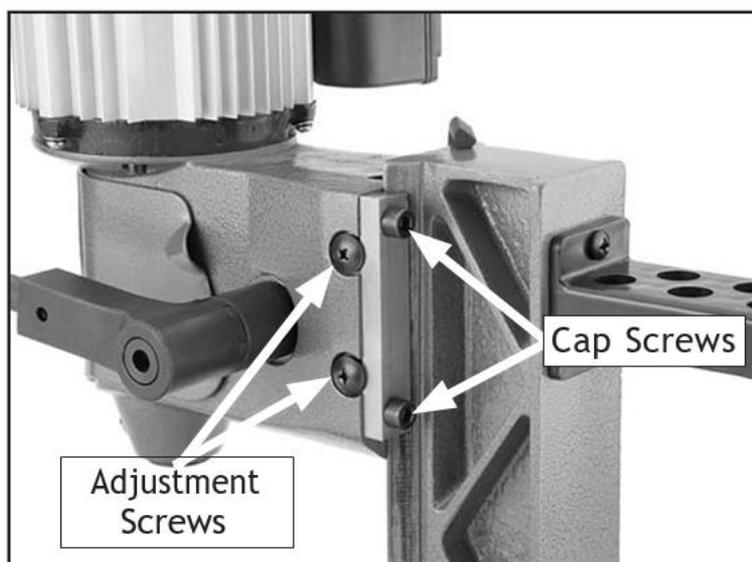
Регулировочные винты для выступа корпуса сверлильного станка.
